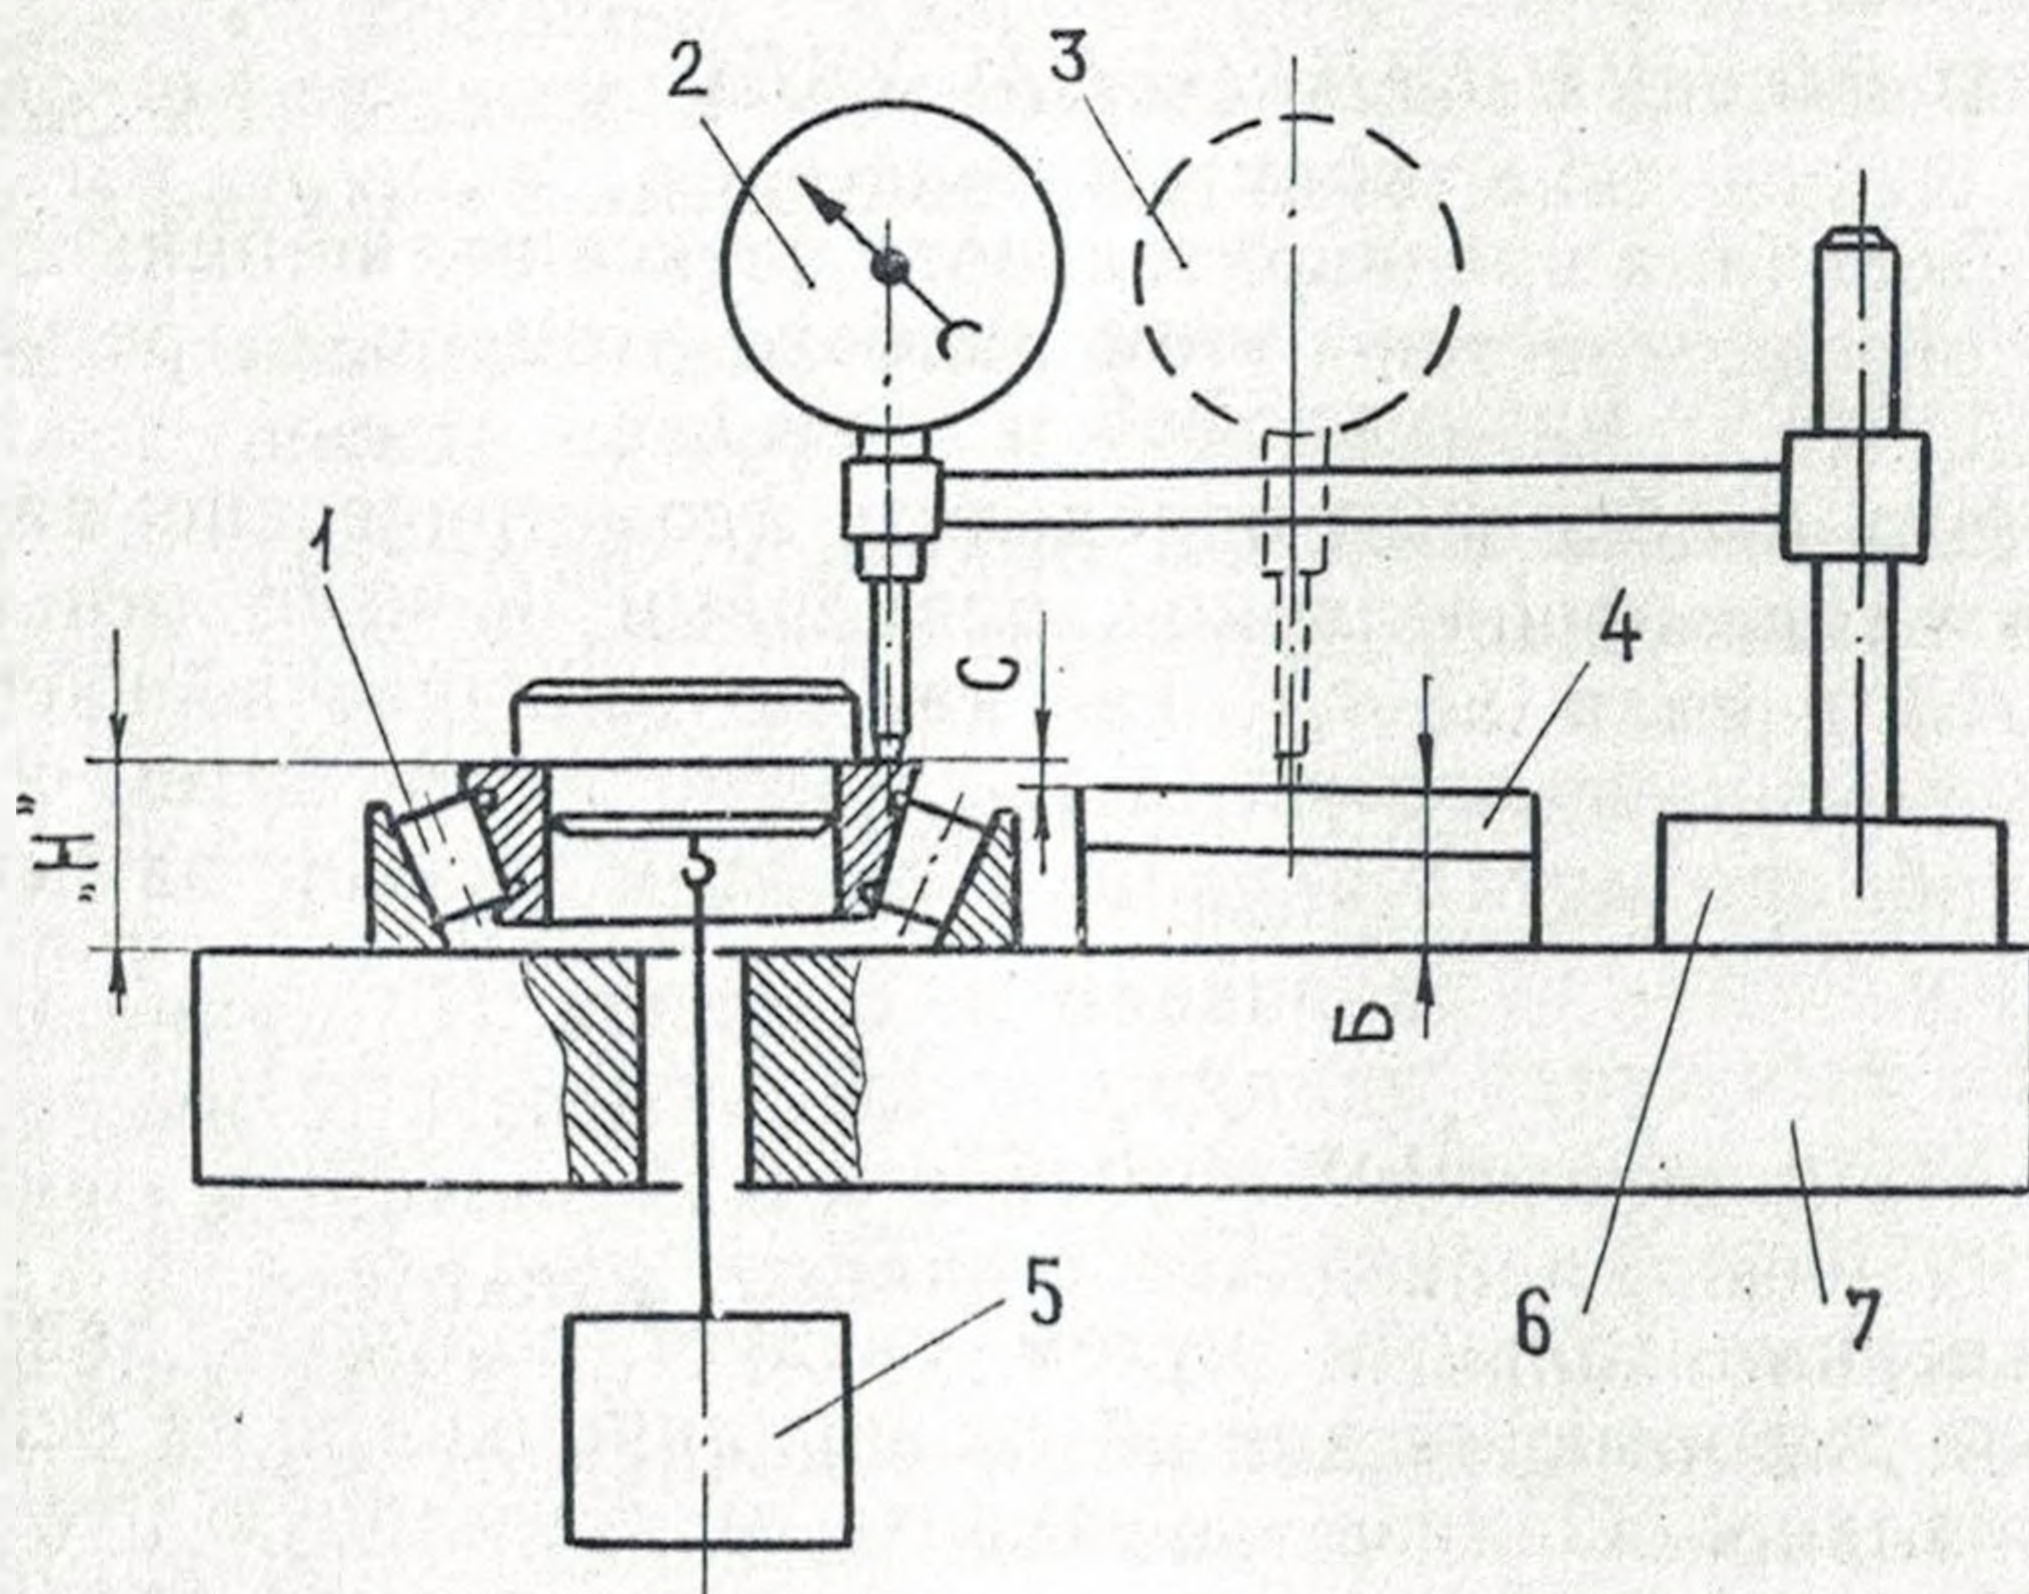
Схема определения монтажной высоты подшипника: 1 — подшипник; 2, 3 — положения индикатора; 4 — блок концевых мер; 5 — груз; 6 — магнитная индикаторная стойка; 7 — опора приспособления
